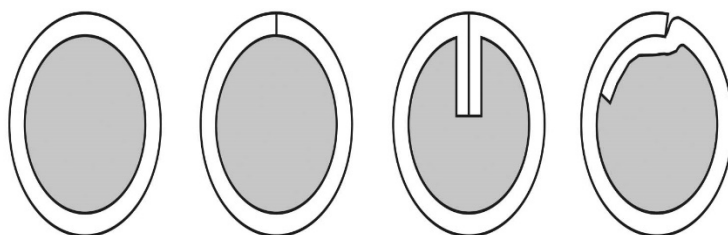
Schematické zobrazení výroby plněných elektrod [31]
